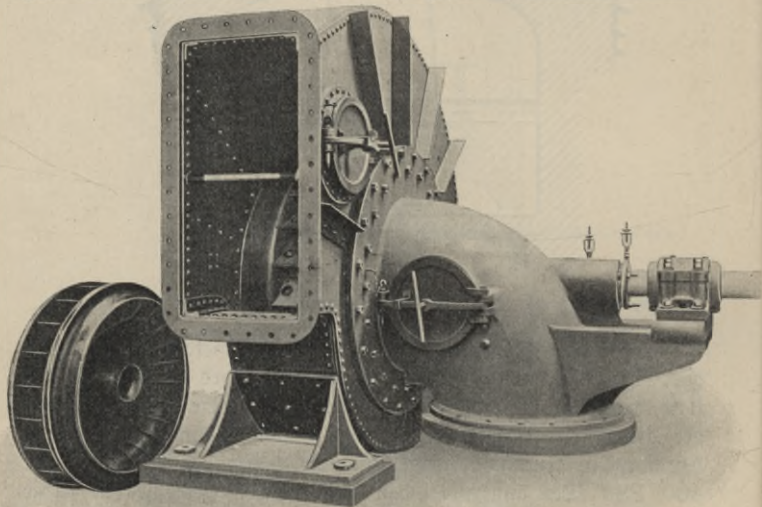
Turbine mit spiralförmigem Gehäuse.
